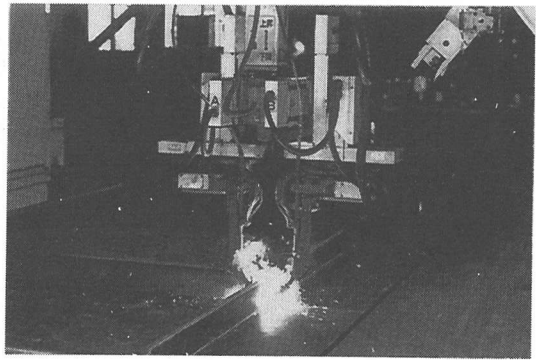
パネル製作ロボットの溶接トーチ部
